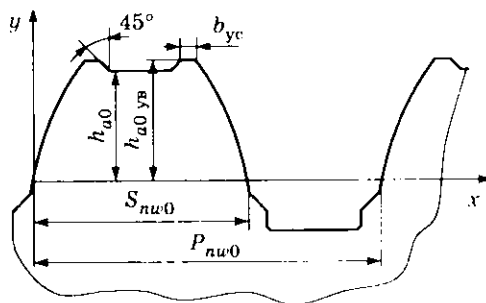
Параметры зубьев червячной шлицевой фрезы
